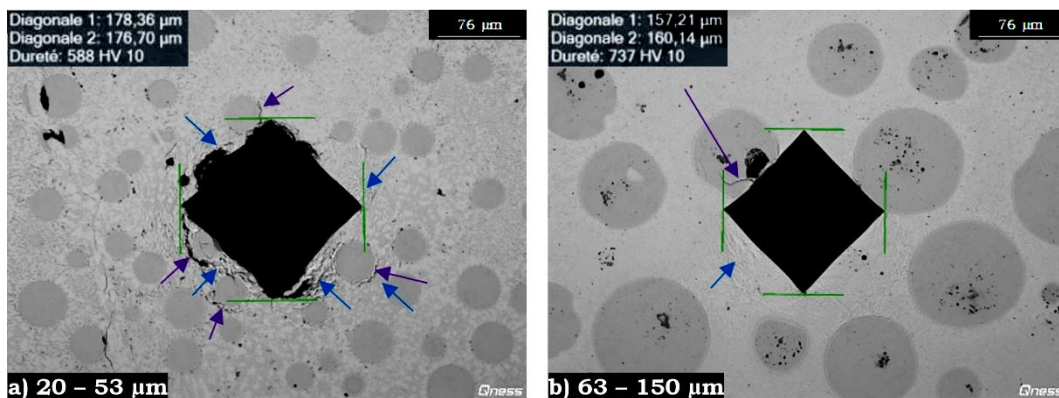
Effet de la granulométrie de la poudre de carbure de tungstène sur la dureté HV10 des revêtements appliqués par laser sur la dureté HV10 à partir du mélange de 60 % massique de poudre de carbure WC ( $DA = 9,9 g/cm^3$ ) avec la matrice à 11 % massique de chrome.
